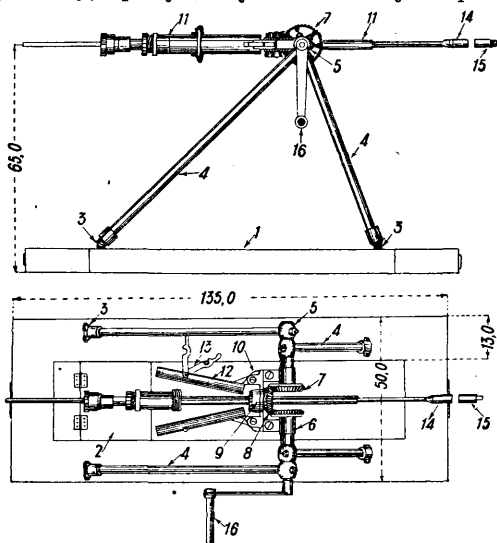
Алмазный буров. 1—деревянная рама, 2—ящики для принадлежностей, 3—проушины, 4—трубчатые ноги, 5—медный шарообразный наконечник, 6—валик, 7—зубчатое колесо, 8—шестерня, 9—втулка, 10—поворотная платформа, 11—зажимная труба, 12—направляющая труба, 13—откидные скобы, 14—колонковая труба, 15—колонковая труба с вращателем и алмазной коронкой, 16—рукоятка станка.
